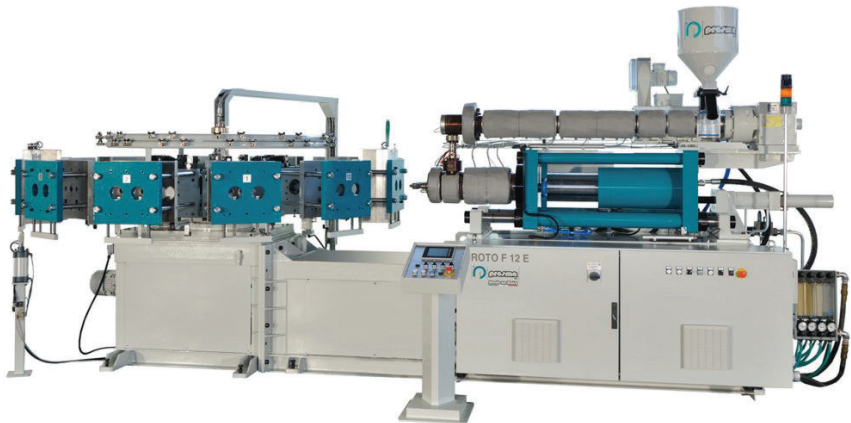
Карусельний багатопозиційний екструзійно-роздувний автомат
